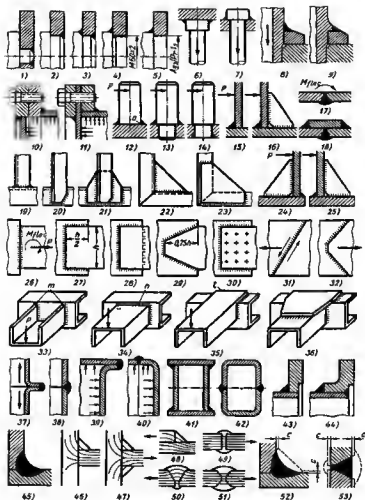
Endurecimiento de las uniones soldadas
